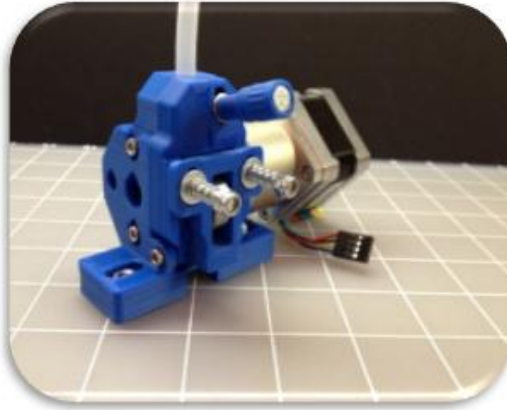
Motor a pasos engranado con cambio rápido de filamento.
